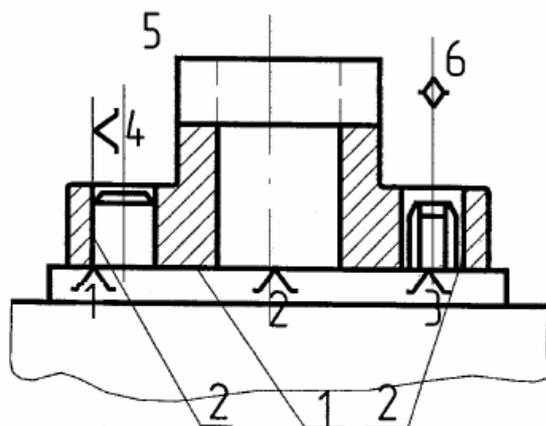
Базирование корпусной заготовки на плоскость и два отверстия
